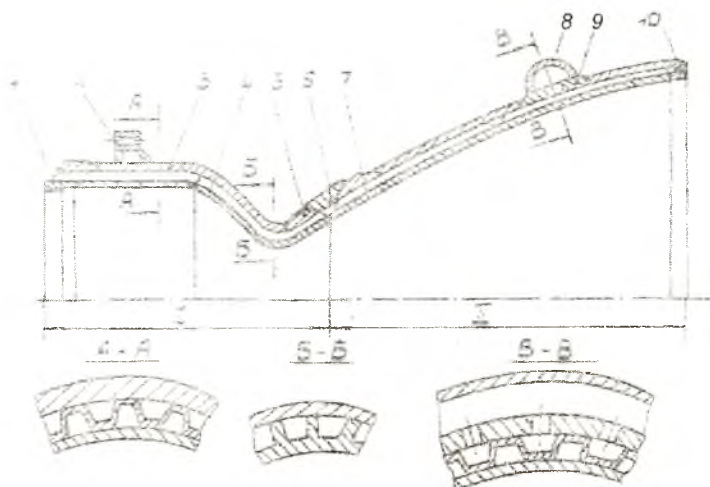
Схема корпуса паяно-сварной камеры: 1 – утолщенное кольцо стенки; 2 – узел крепления камеры к раме ЛА; 3 – рубашка; 4 – стенка; 5 – переходное кольцо; 6 – соединительное кольцо; 7 – гофрированная проставка; 8 – обечайка коллектора; 9 – распределительное кольцо; 10 – замыкающее кольцо
